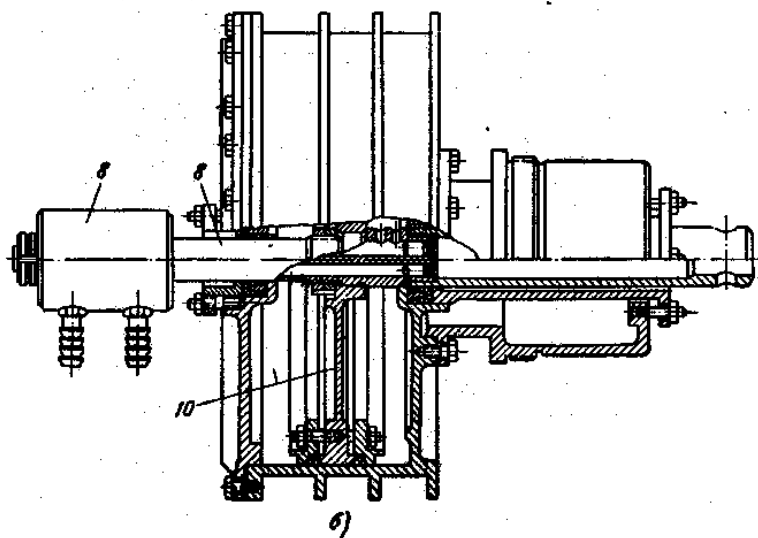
Конструкция цапговых патронов резьбофрезерных станков:
